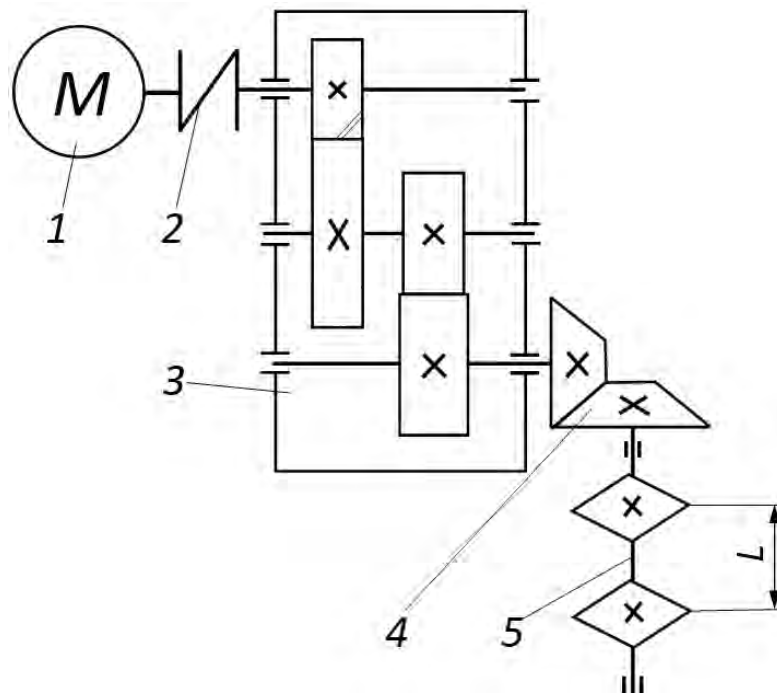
Схема привода цепного конвейера (вид сверху): 1 – асинхронный электродвигатель; 2 – муфта упругая с резиновой звездочкой; 3 – редуктор двухступенчатый цилиндрический с косозубой и прямозубой передачами; 4 – открытая прямозубая коническая передача; 5 – приводной вал с двумя приводными звездочками
